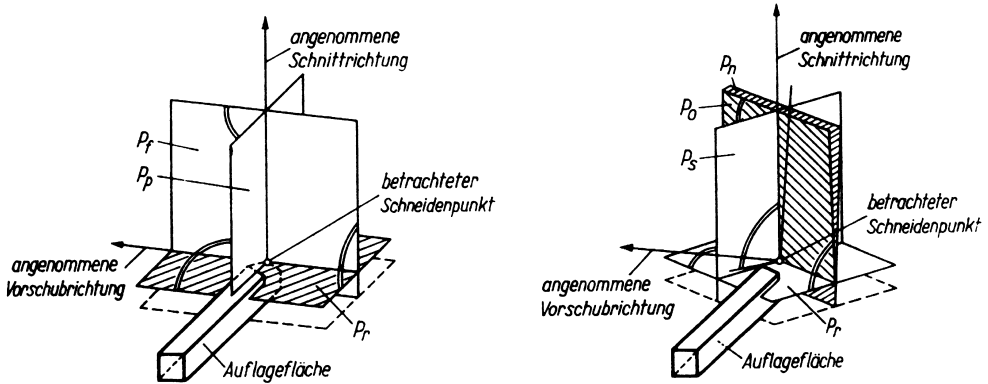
Ebenen im Werkzeug-Bezugssystem (nach DIN 6581)
